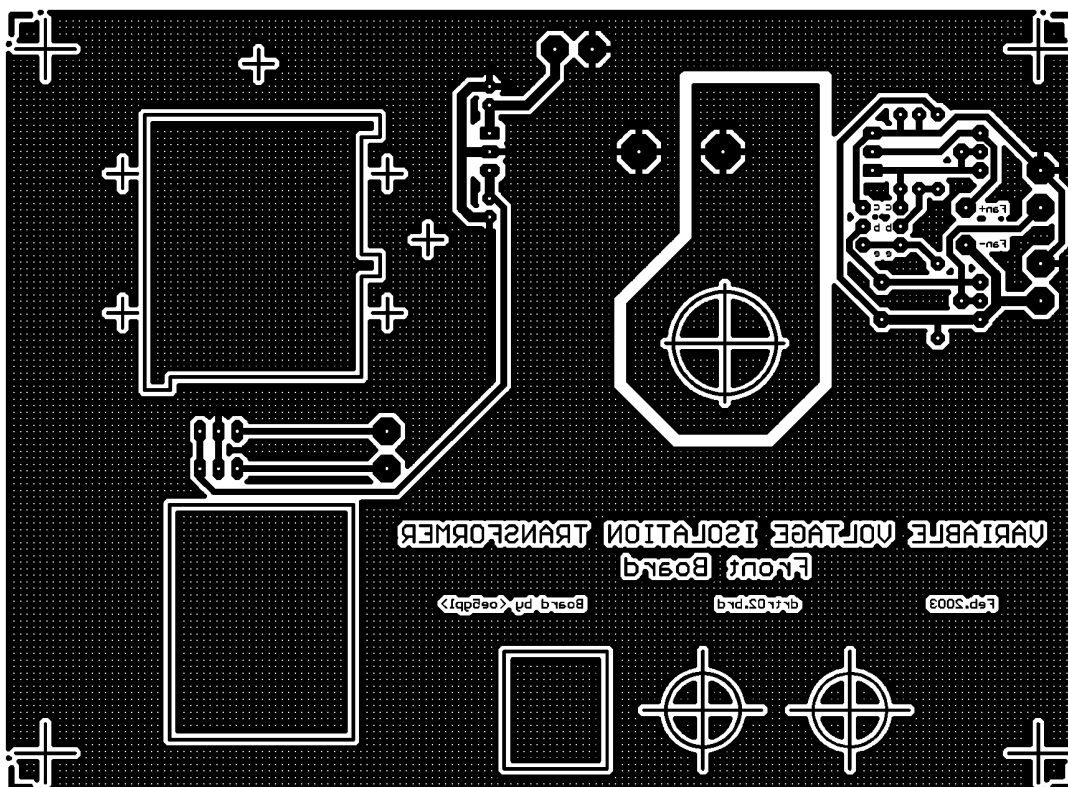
Leiterplatten-Layout der frontseitigen Montageplatte (nicht maßstäblich)
